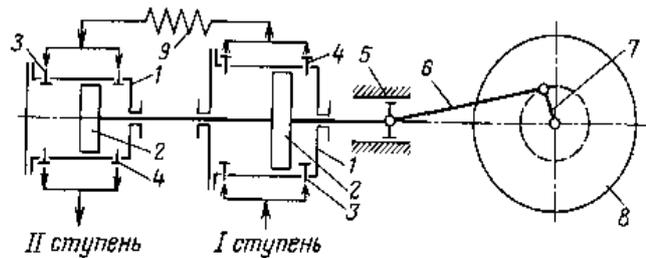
Двухступенчатый компрессор (тандем – цилиндры расположены по одной оси)
